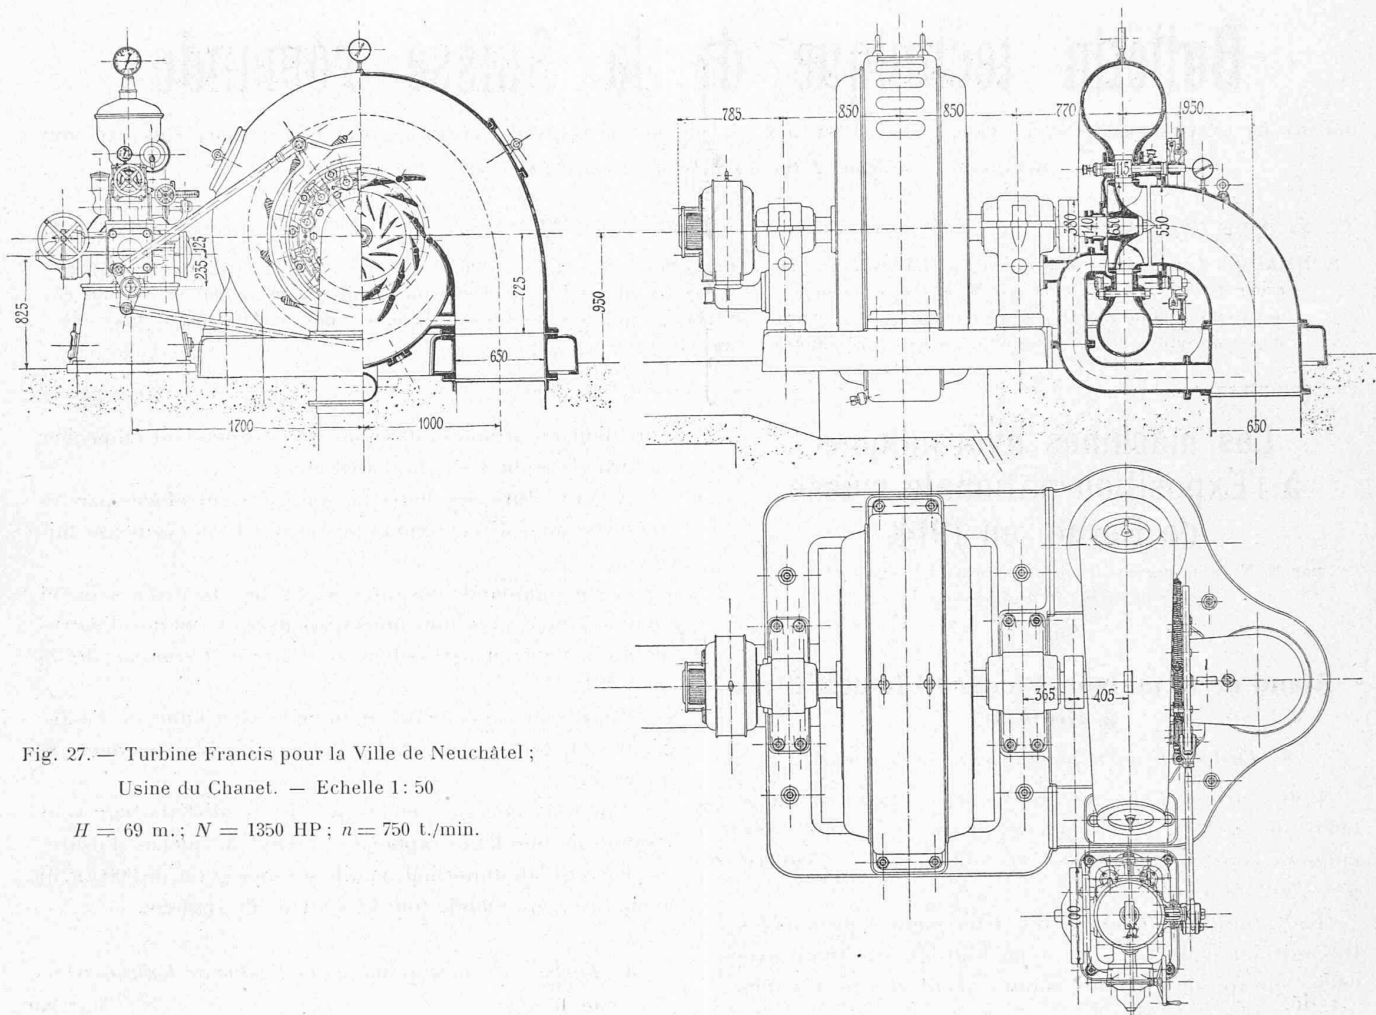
Turbine Francis pour la Ville de Neuchâtel ;
